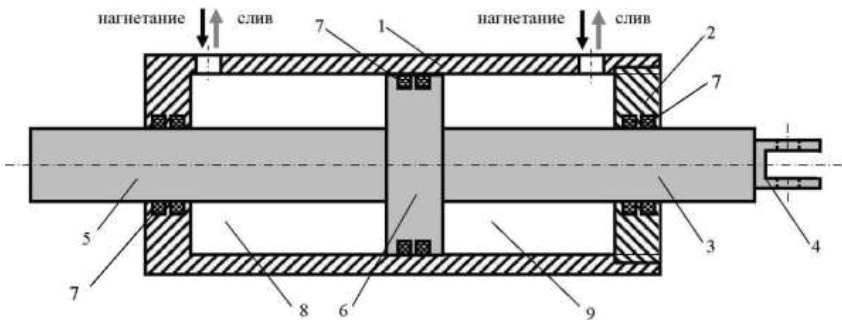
Схема силового гидроцилиндра с ложным штоком, где 1- корпус; 2- крышка; 3,5- шток; 4- проушина; 6- поршень; 7- уплотнительное кольцо; 8,9- полости гидроцилиндра
